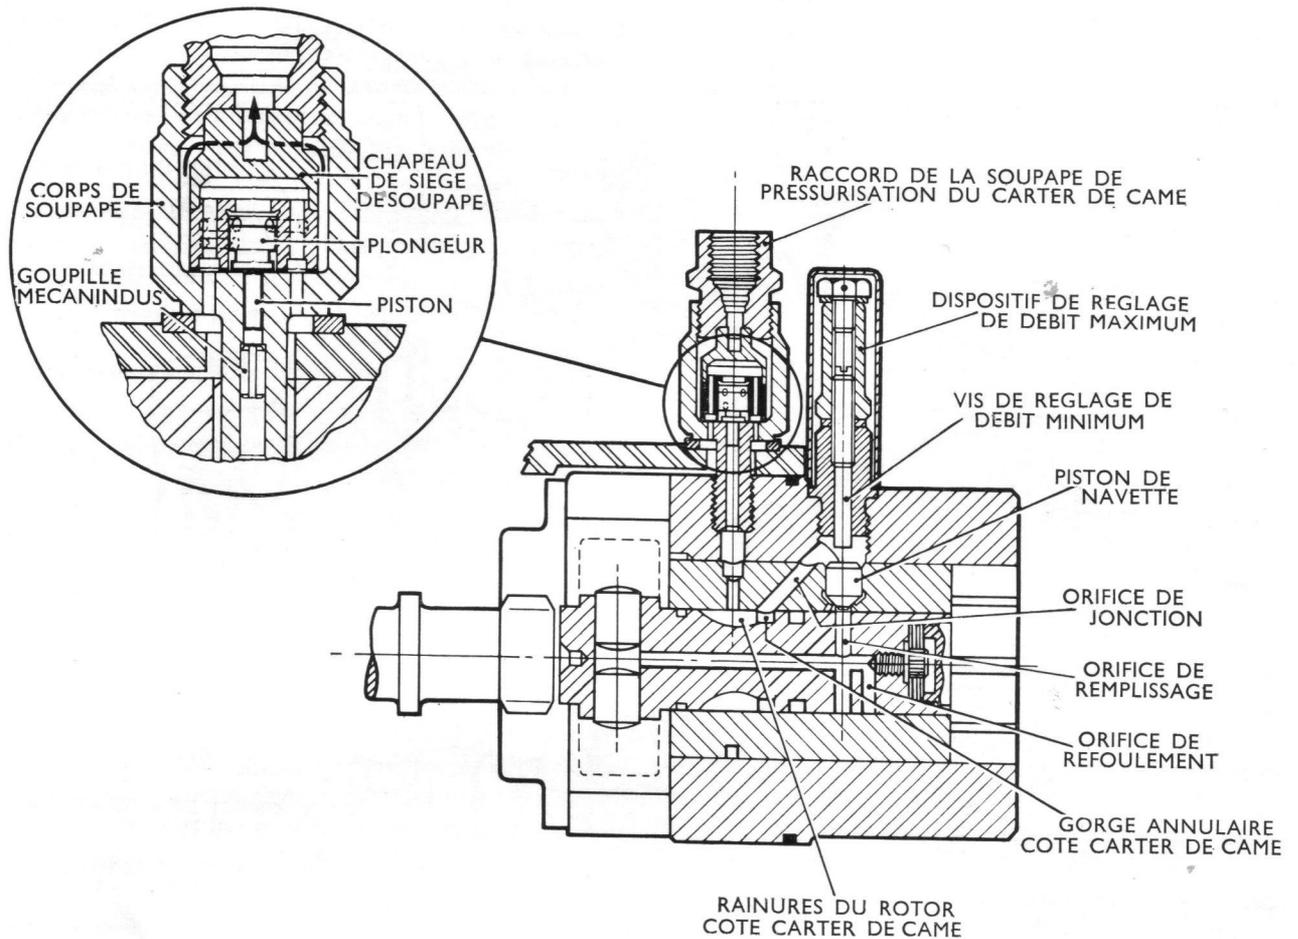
Soupape de pressurisation du carter de came et dispositif extérieur de réglage de débit maximum
